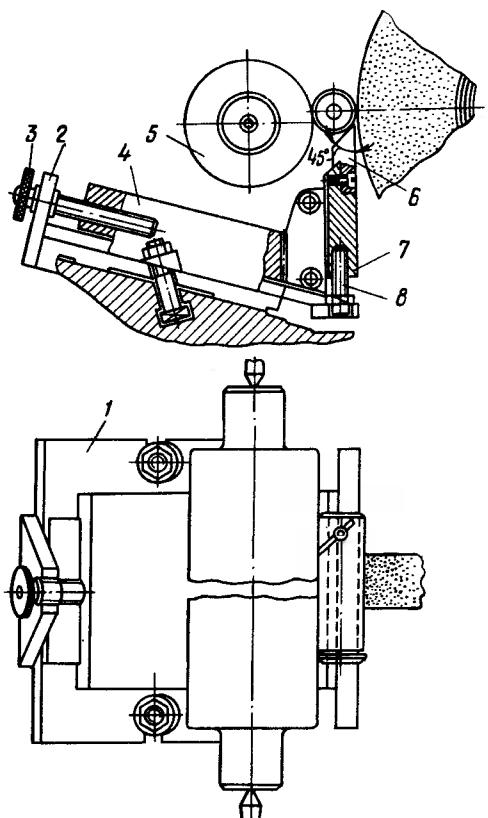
Суппортно-шлифовальное приспособление для восстановления поршневых пальцев
